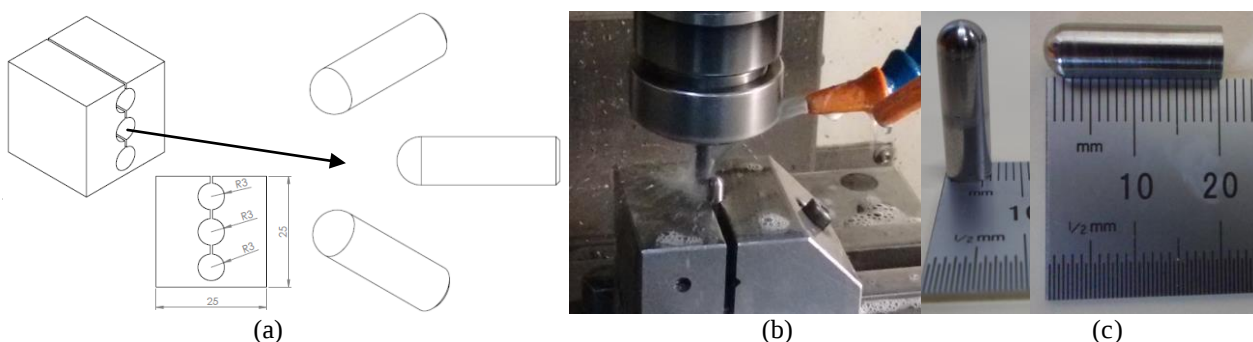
Pinos de Ferro Fundido Nodular (a) – desenho esquemático corte eletro-erosão (b) – Usinagem em centro de usinagem por interpolação (c) – Pino acabado (O autor, 2017)
